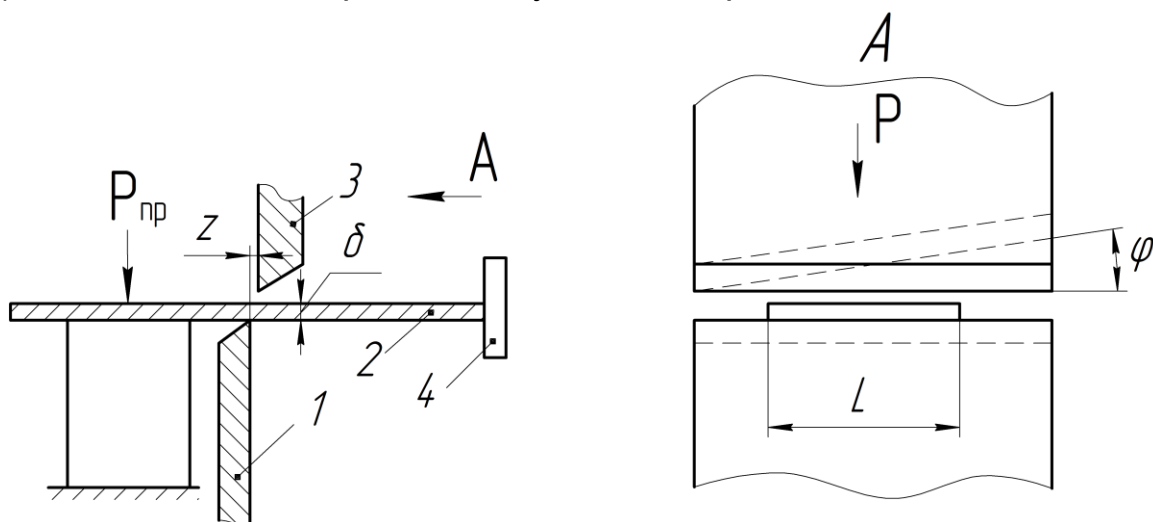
Різання паралельними та гільйотинними ножицями: 1 – нижнє лезо; 2 – заготовка; 3 – верхнє лезо; 4 – упор
